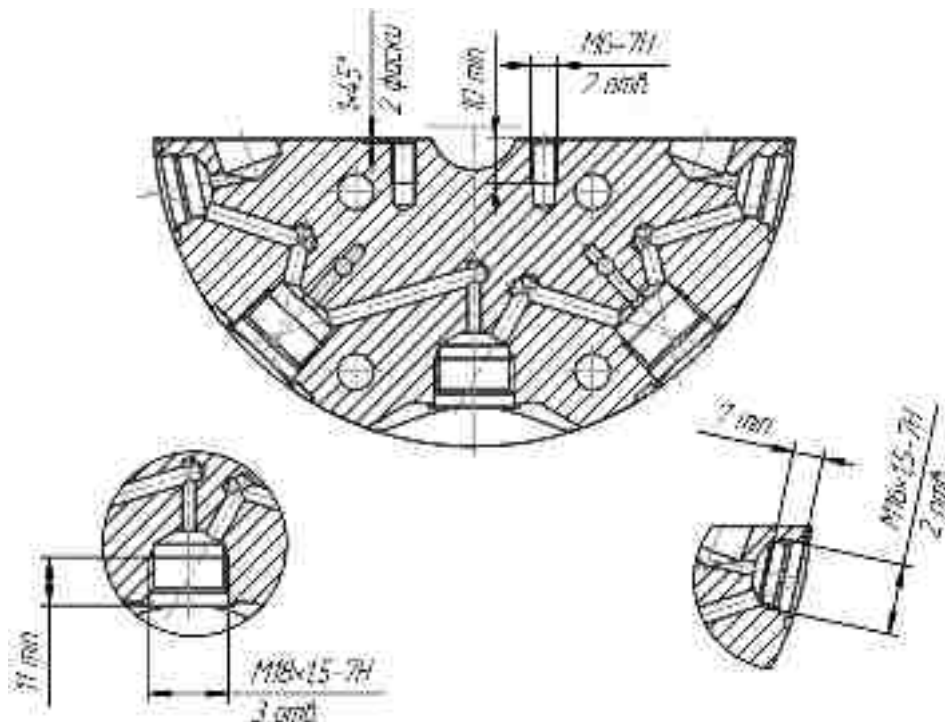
Эскиз контроля калибрами-пробками резьбовыми ПР-НЕ
